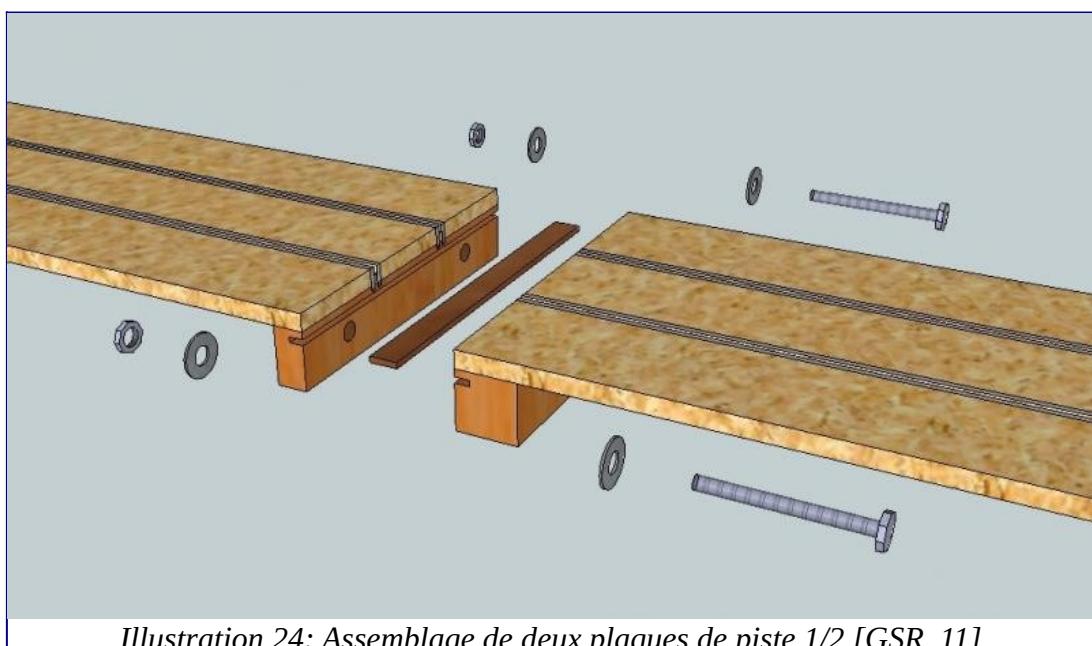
Assemblage de deux plaques de piste 1/2 [GSR_11]
